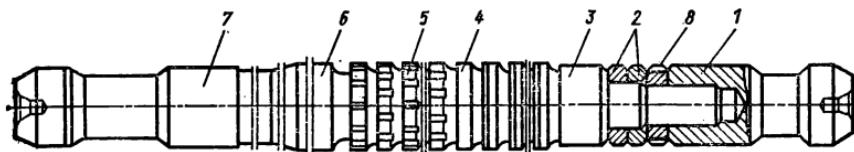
Протяжка круглая сборная быстрорежущая с выглаживающими зубьями из твердого сплава
